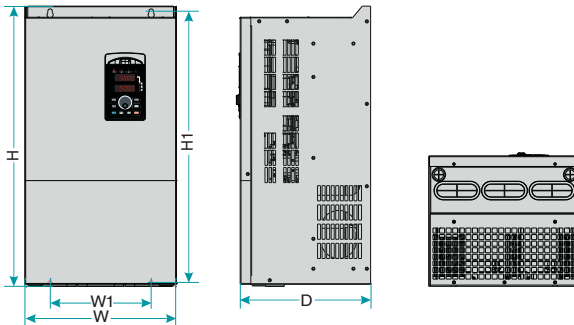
55KW~110KW机型外型尺寸及安装尺寸示意图
